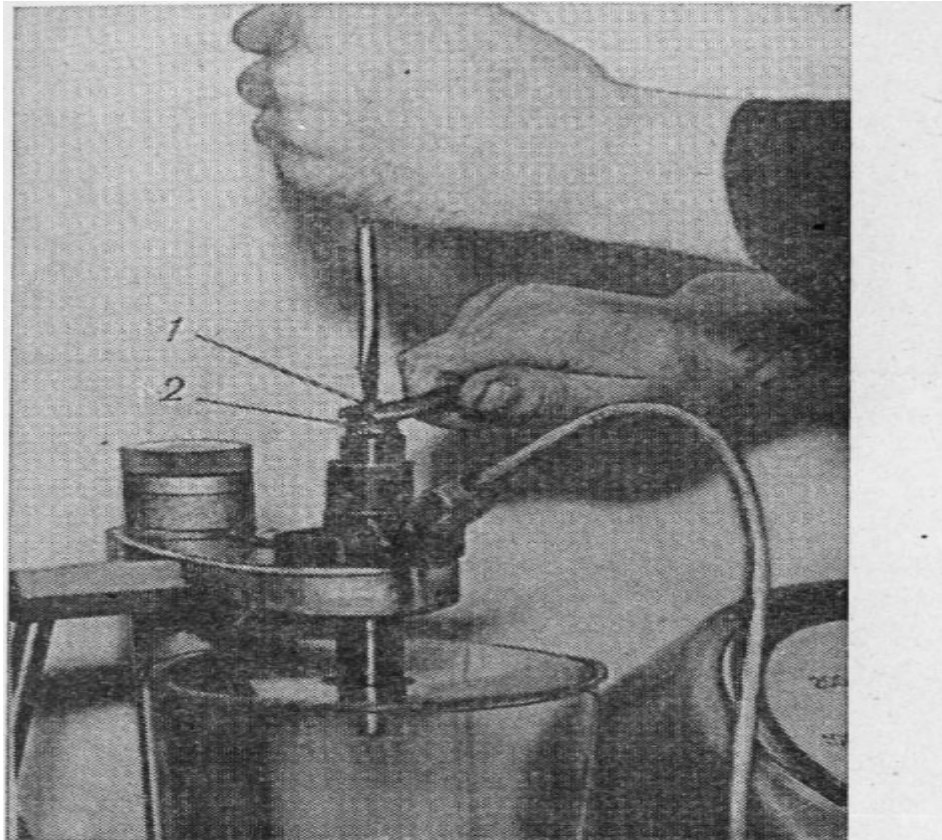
Регулировка форсунки: 1 — регулировочный винт; 2 — контргайка
